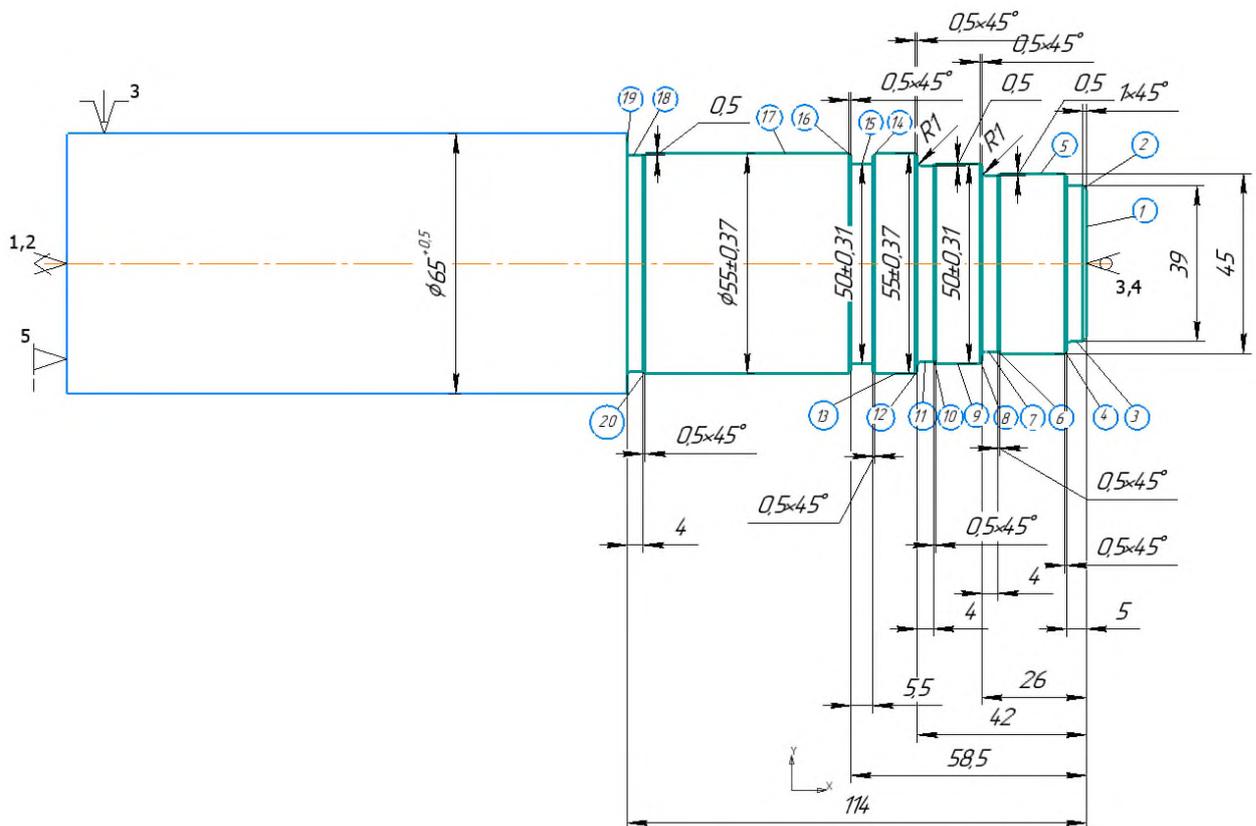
Перший спосіб базування та закріплення заготовки на операції 025.
